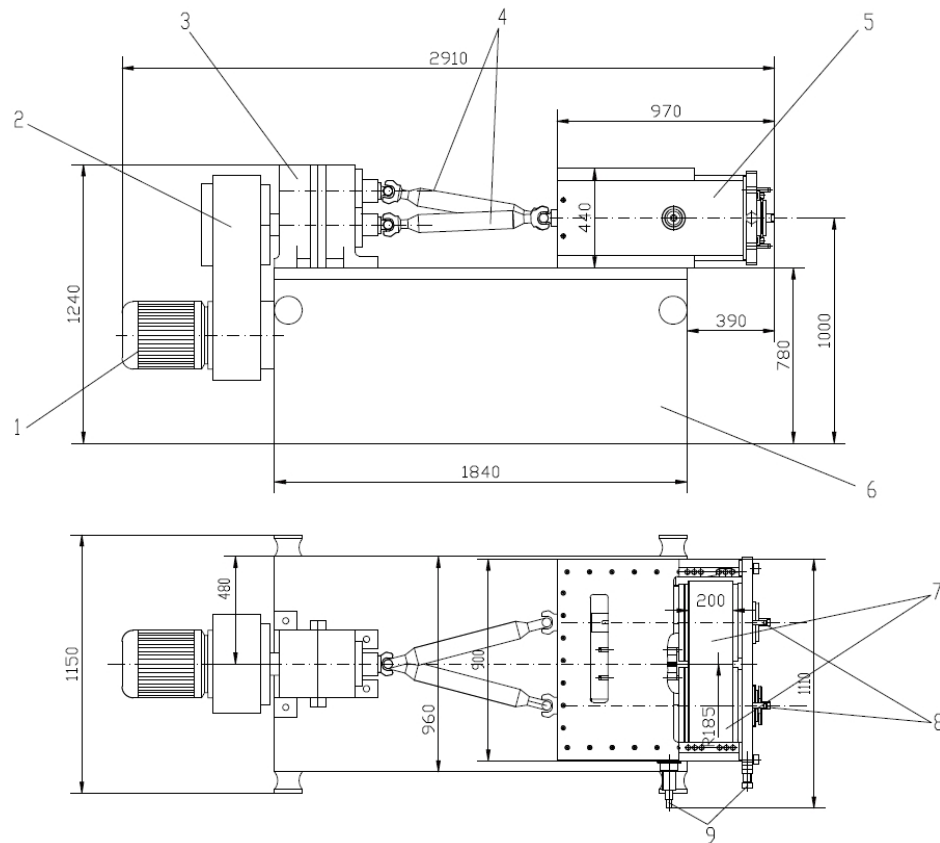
Експериментальна установка валкового розливу-прокатки в Падерборнському Університеті: 1 – двигун; 2 - редуктор; 3 – шестеренна кліть; 4 - шпинделі; 5 – кліть валкового розливу-прокатки; 6 - стіл; 7 – валки-кристалізатори; 8 – патрубки подачі і відведення охолоджуючої рідини; 9 – регулювальні гвинти [80]
